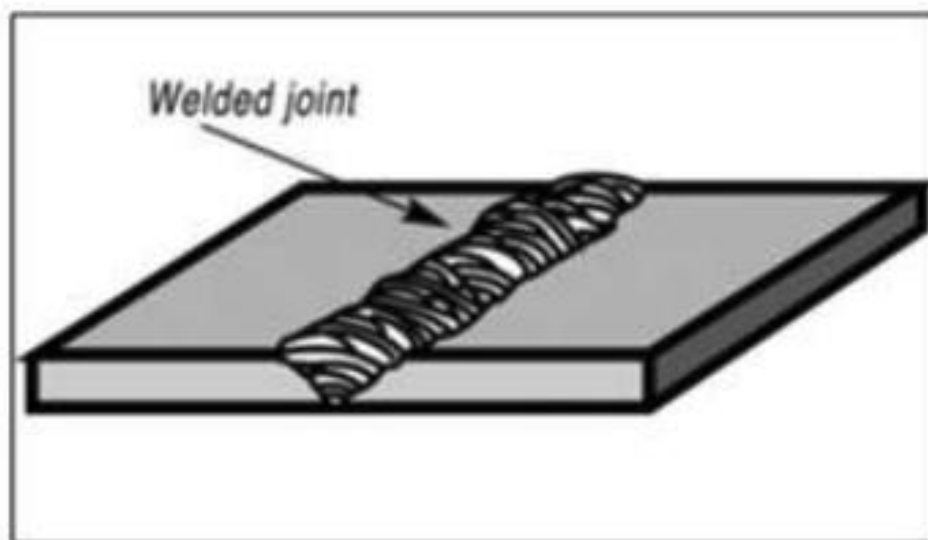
Placa soldada mediante soldadura, adaptado de Albloushi y Albloushi (2019), bajo licencia CC BY-SA 4.0. (3)
